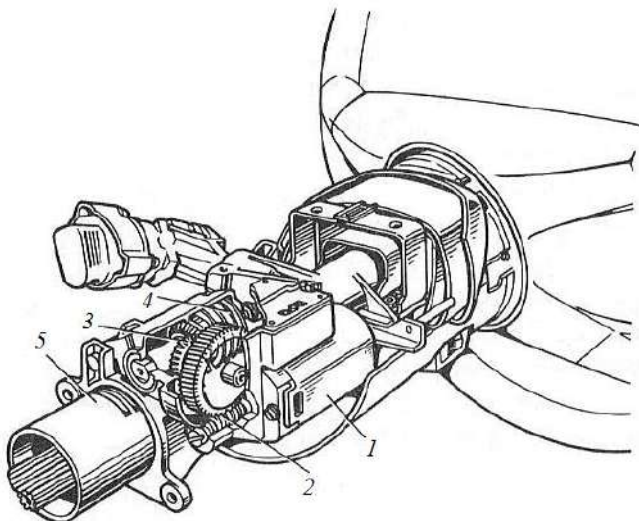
Рульова колонка з електричним приводом регулювання положення рульового колеса:
